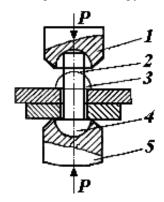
Схема образования заклепочного соединения: I – оправка; 2 – стержень заклепки; 3 – замыкающая головка заклепки; 4 – закладная головка; 5 – поддержка
